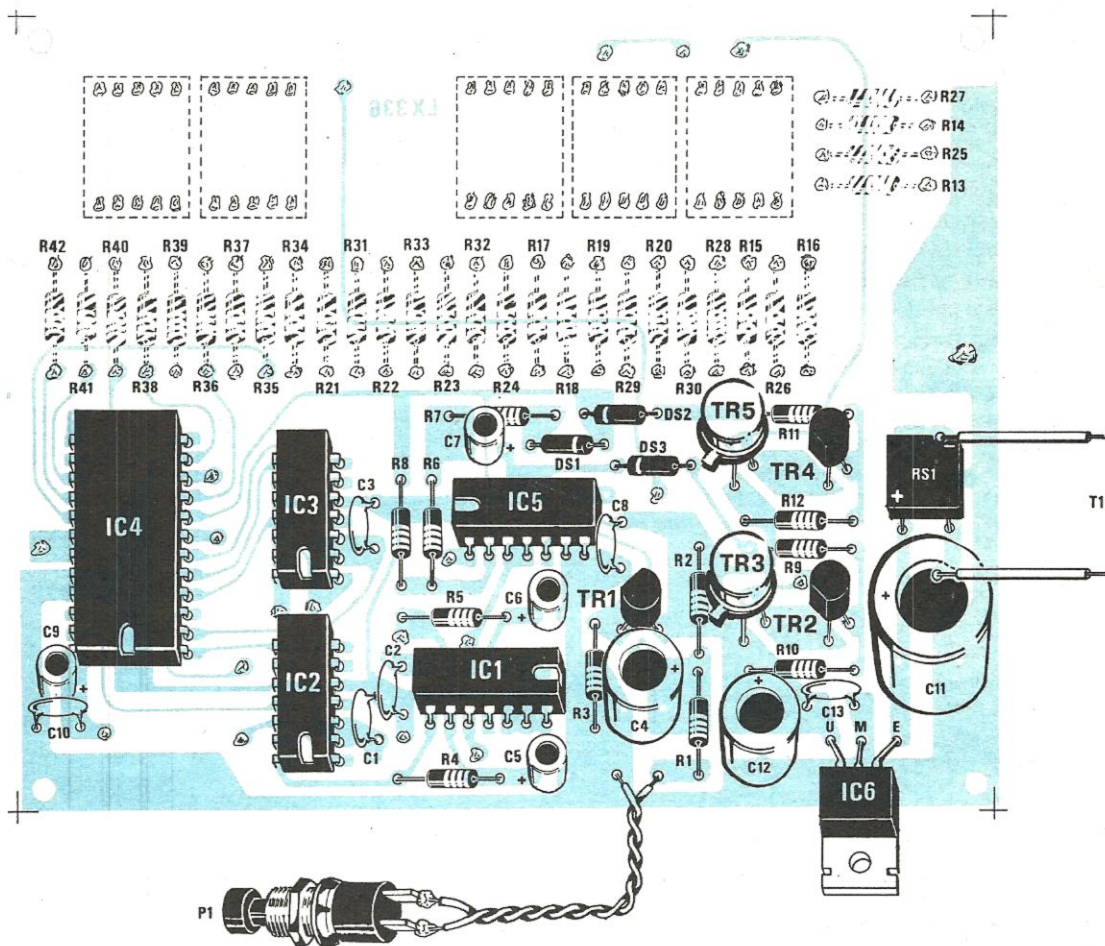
In questo disegno è possibile vedere come vanno montati sul lato principale del circuito stampato gli integrati e i transistor richiesti per questo progetto. Per gli integrati ricordatevi di utilizzare come al solito gli appositi zoccoli perché così facendo, in caso di guasto, è possibile sostituirli con facilità senza danneggiare le piste di rame. I display e le resistenze ad essi collegate andranno invece sistemati sulla facciata opposta ricordandosi che i terminali di alcune resistenze servono anche da ponticello di collegamento fra le piste inferiori e superiori.
